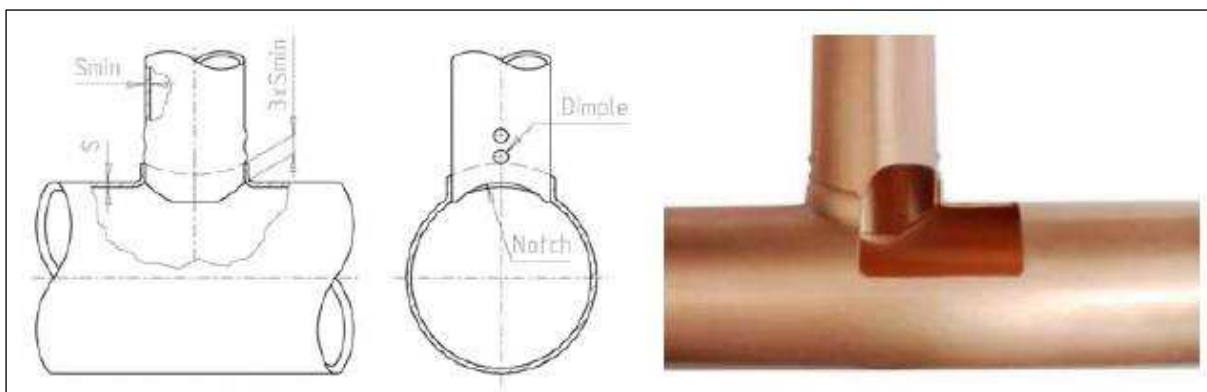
Detail překlátovaného spoje pomocí zářežek [5]
